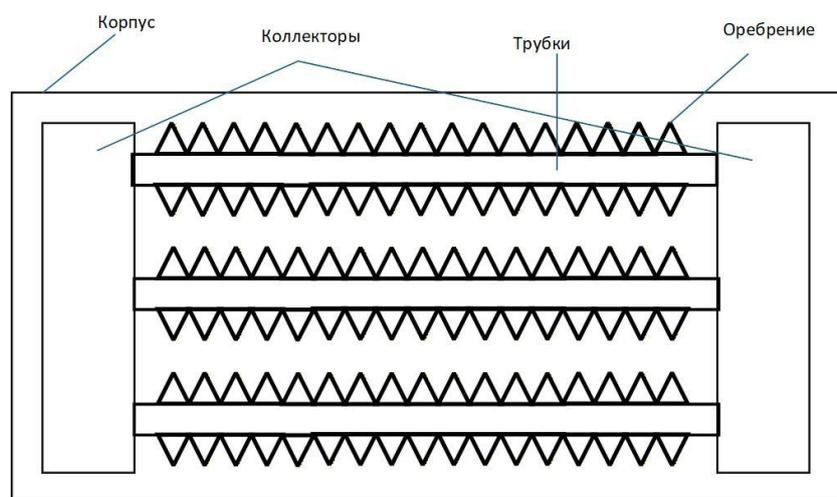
Ребристо-трубный воздухонагреватель (схема автора)
